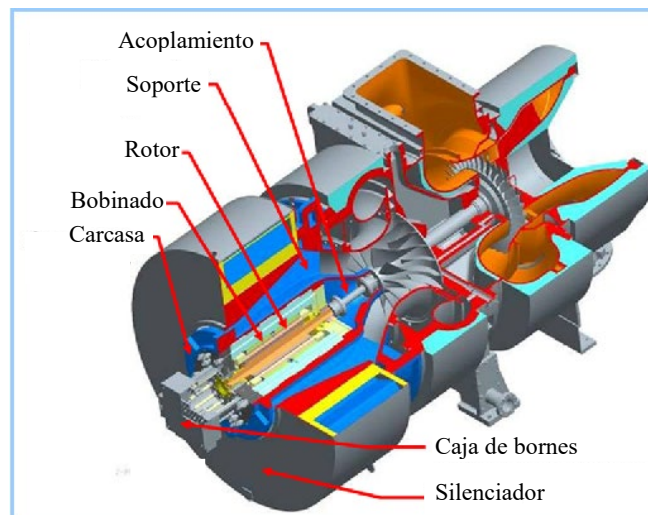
Turbocompresor con alternador acoplado [69].
